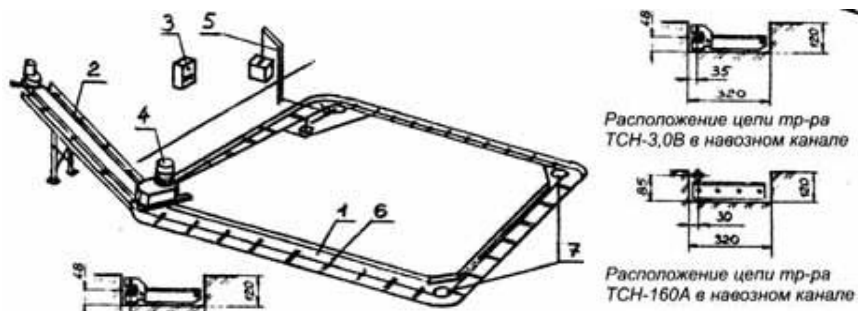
Схема транспортера ТСН: 1 – горизонтальный транспортер; 2 – наклонный транспортер; 3 – устройство управления; 4 – привод; 5 – натяжное устройство; 6 – цепь со скребками; 7 – устройство поворотное.
